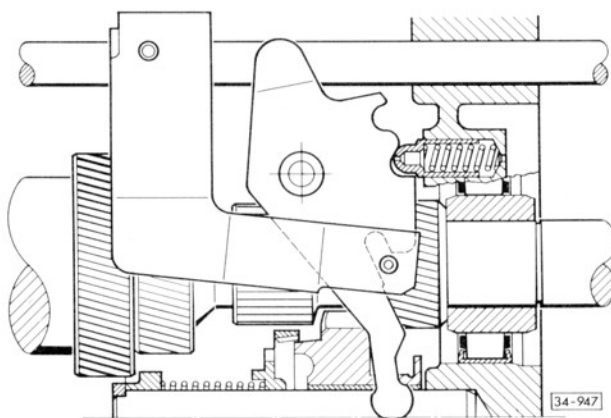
Einbaulage Rückwärtsgang – Arretierung
